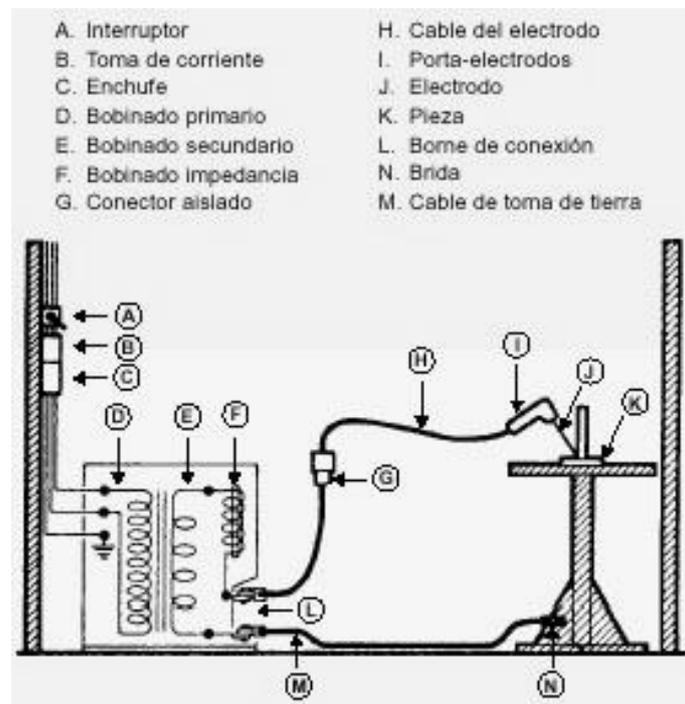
Instalación segura de un puesto de soldadura CA con transformador
